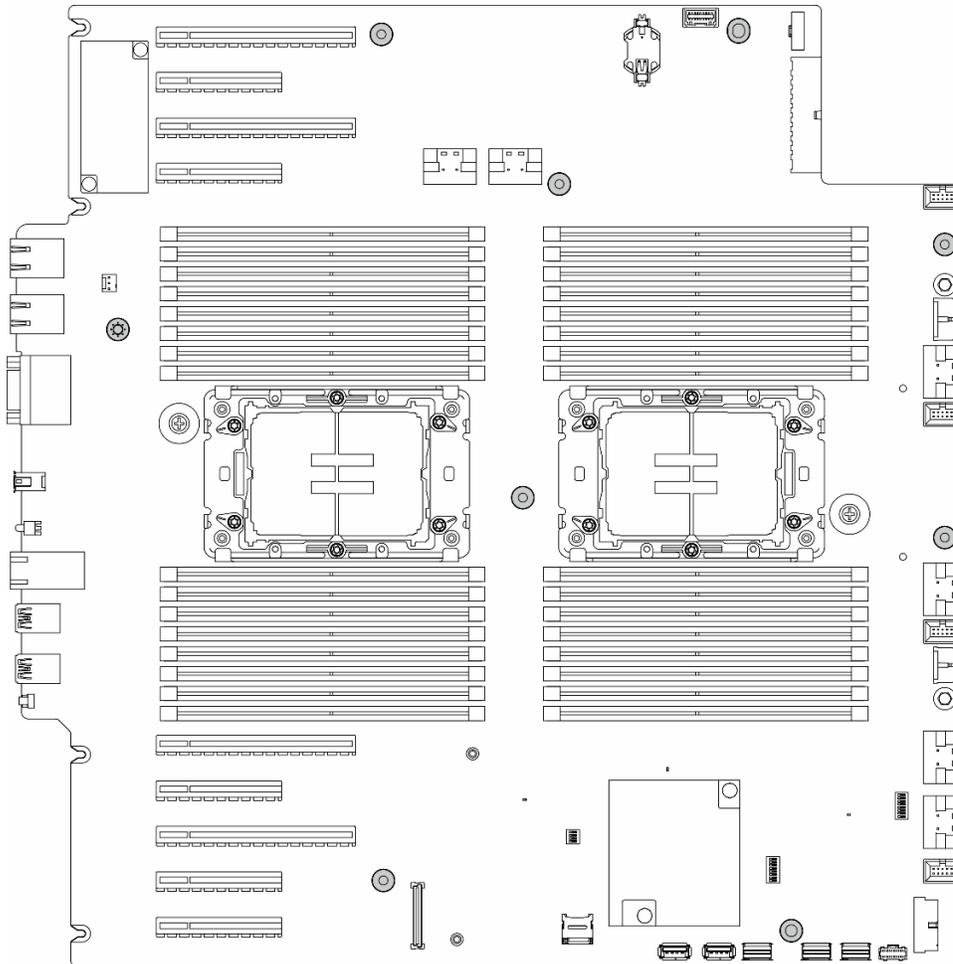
Entfernen der Schrauben an der Systemplatine
